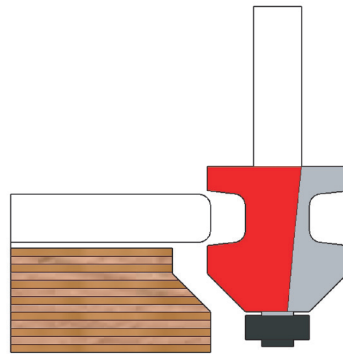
Spezieller Fräser für Ausschnitte mit großem Eckenradius
